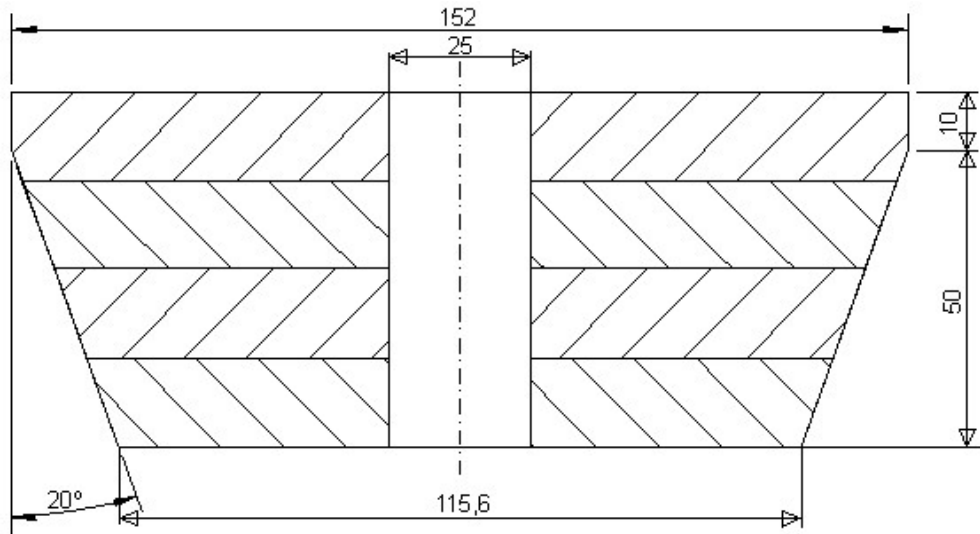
Desen penetrator cu unghi la centru de 40°
